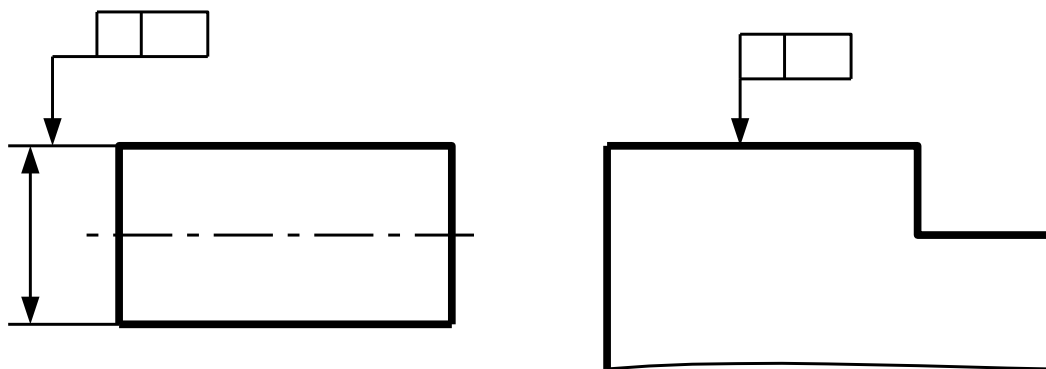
Нанесения размера допуска, относящегося к поверхности или ее профилю
